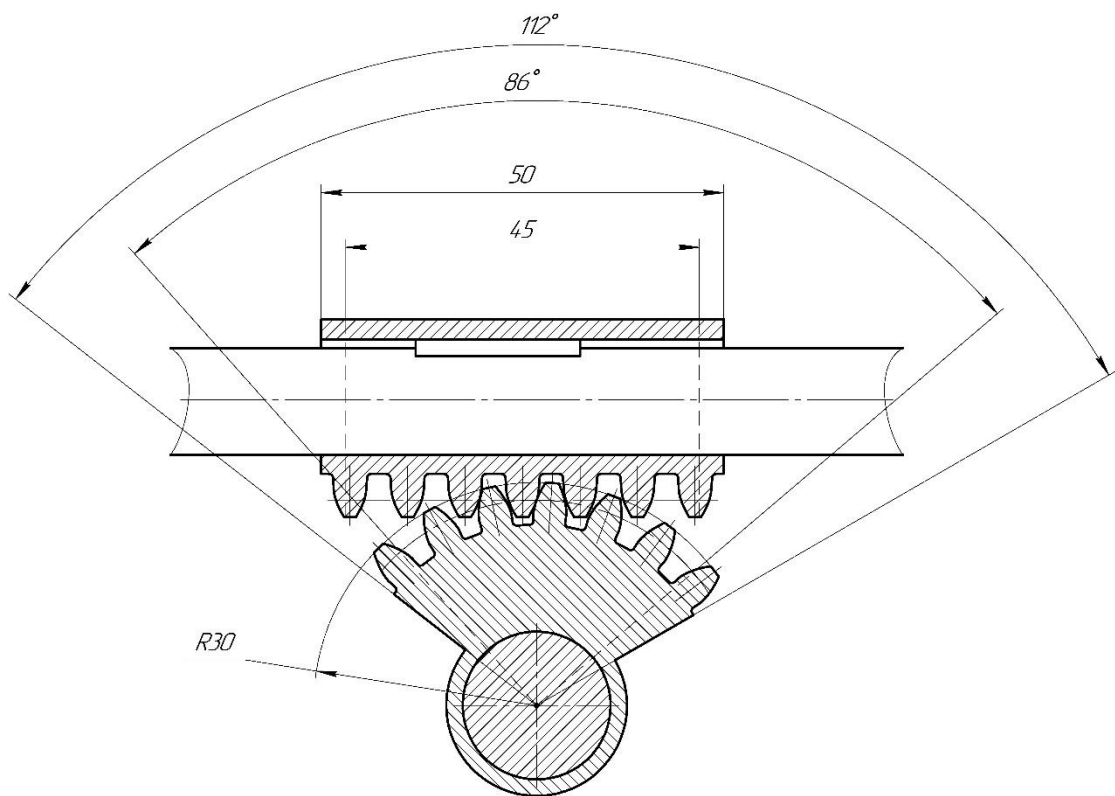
Механізм переключення блоків коробки швидкостей з двома зубчатыми колесами
